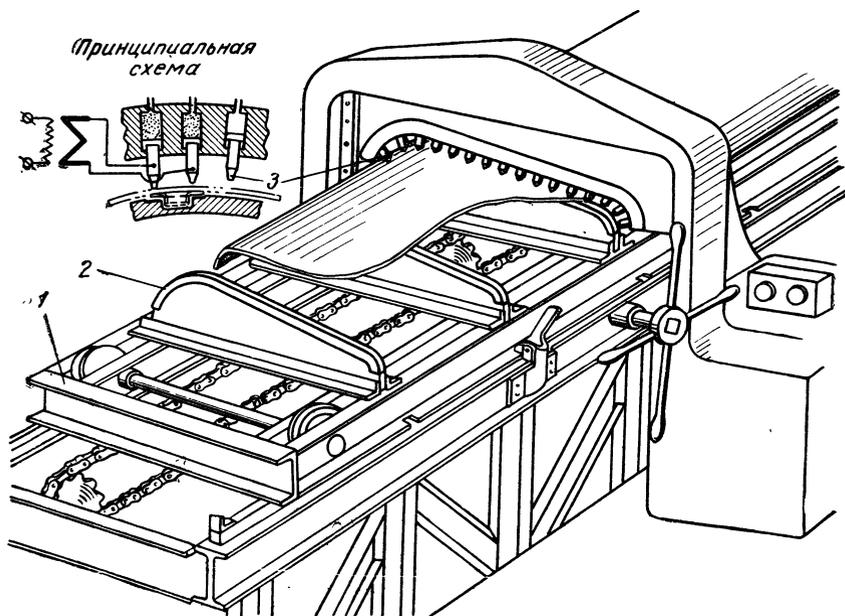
а. Приспособление для точечной сварки с помощью рычага.
